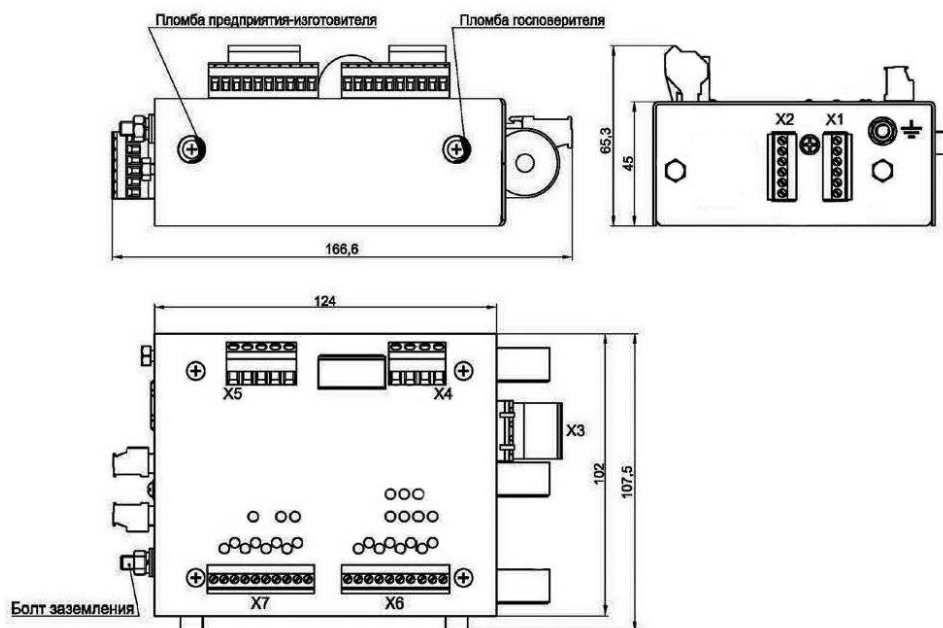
Внешний вид и габаритные размеры устройства
